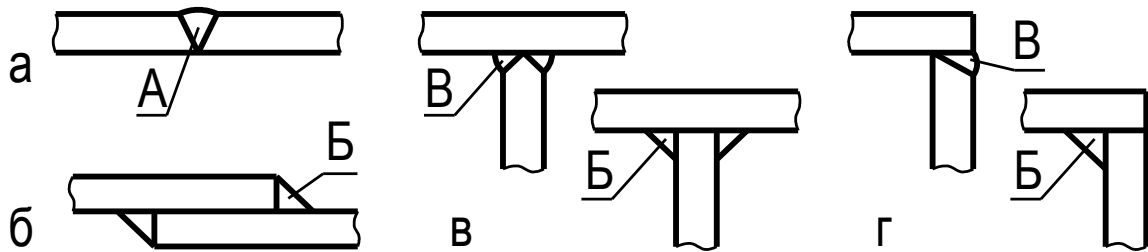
Види зварних з'єднань і типи зварних швів
